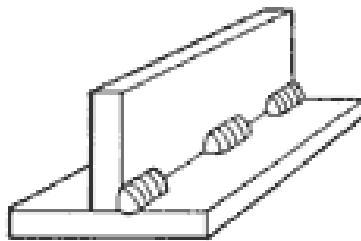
Esquema de una soldadura intermitente ²¹
